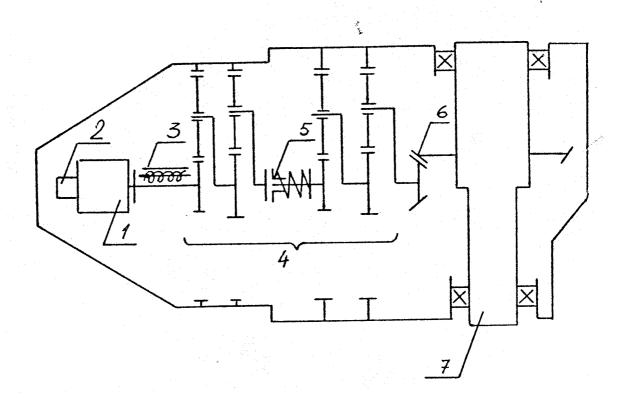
Шарнир манипулятора: 1 — электродвигатель постоянного тока; 2 — тахогенератор; 3 — электромагнитный тормоз; 4 — четырехступенчатый планетарный редуктор; 5 —моментная муфта; 6 — коническая пара; 7 — выходной вал.
